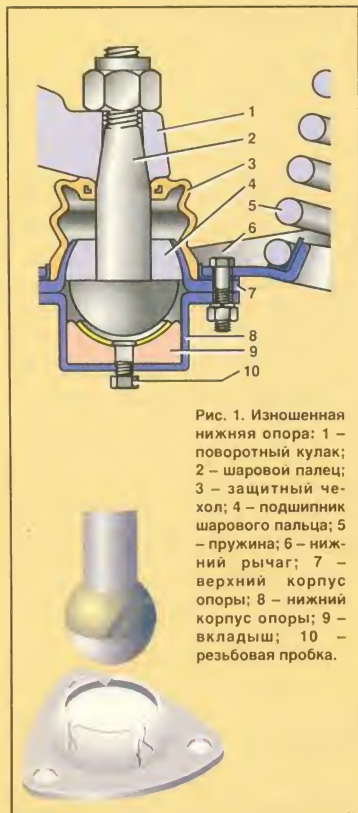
Изношенная нижняя опора: 1 – поворотный кулак; 2 – шаровой палец; 3 – защитный чехол; 4 – подшипник шарового пальца; 5 – пружина; 6 – нижний рычаг; 7 – верхний корпус опоры; 8 – нижний корпус опоры; 9 – вкладыш; 10 – резиновая пробка.
